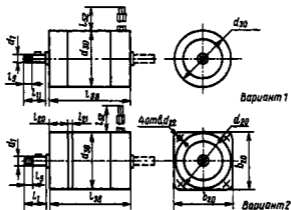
Габаритные и установочные размеры двигателя АСД-3
